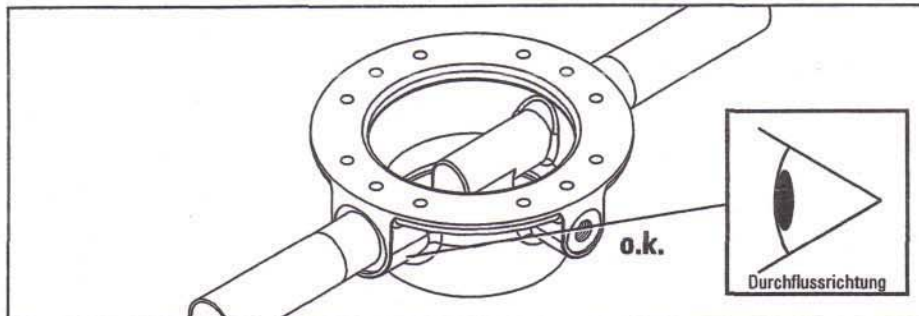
Druckminderer, Montage Anschweißenden, Anschweißen des Gehäuses (Abbildung zeigt Ventilgehäuse Art. DM330362).
